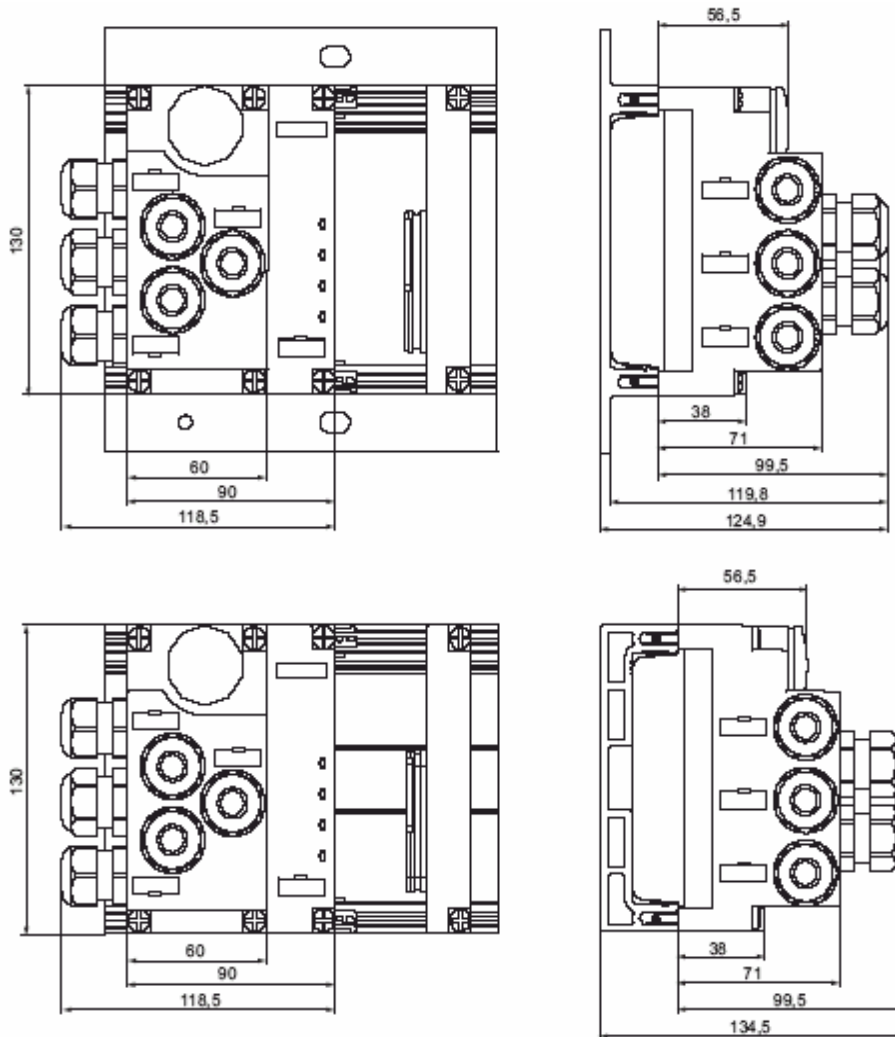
Габаритные размеры интерфейсного модуля с соединительным модулем CM IM DP Direkt
